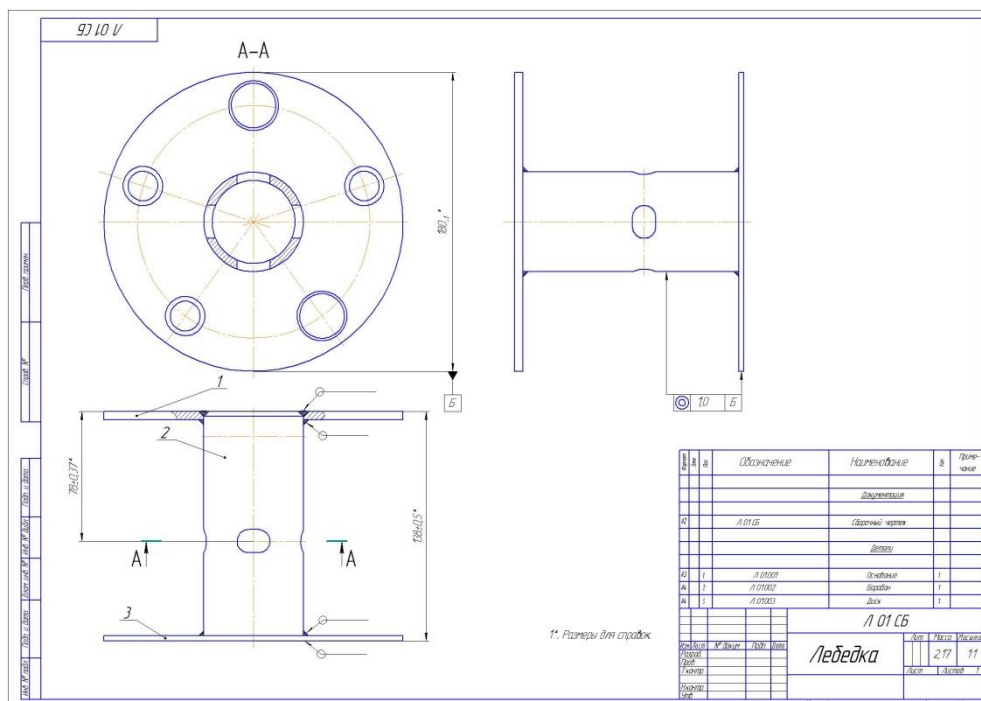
Скорректированный сборочный чертеж самовытаскивателя
